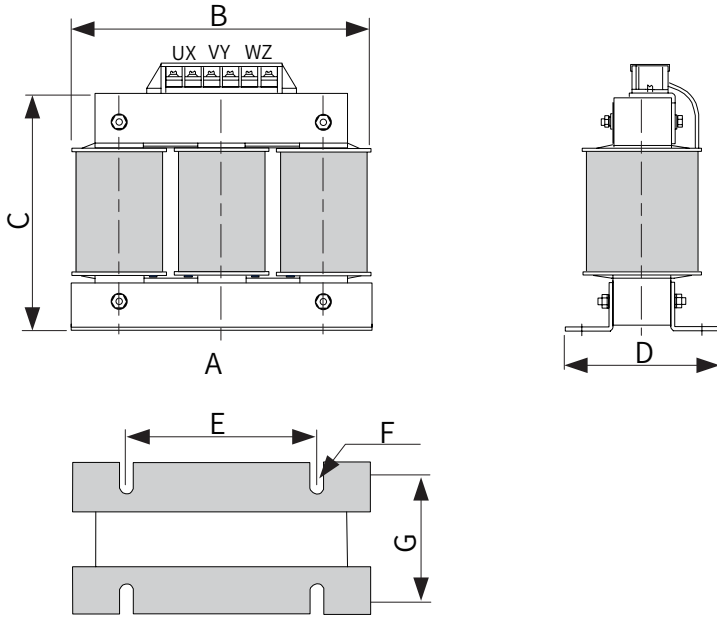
Размеры выходного реактора переменного тока 20 А
